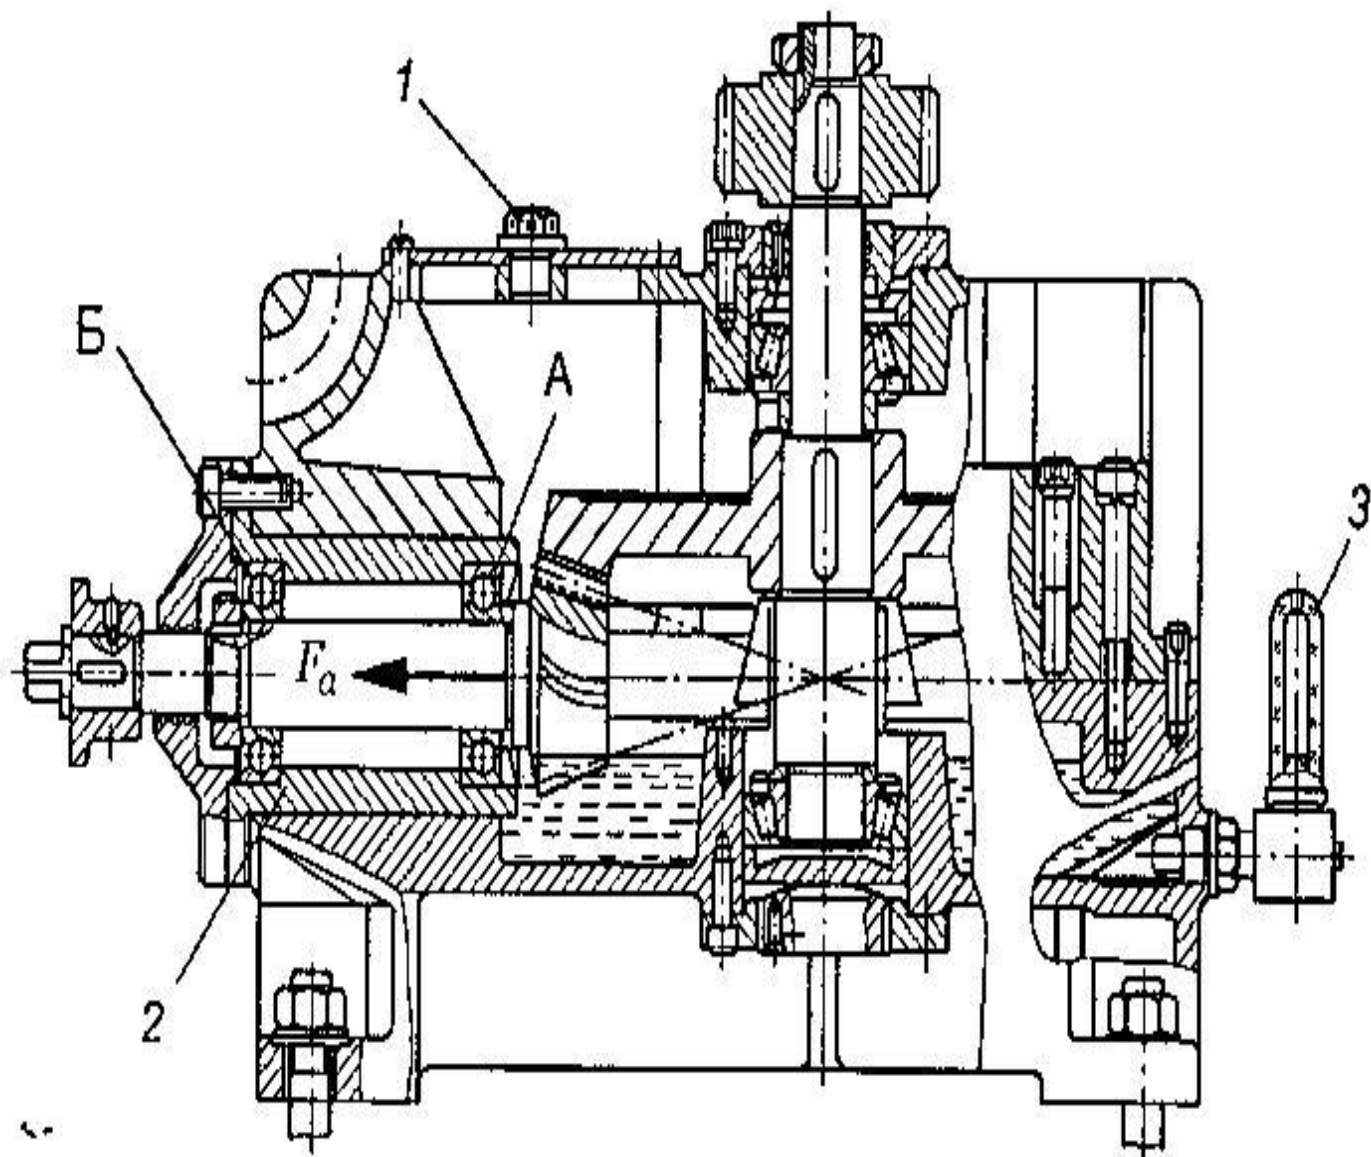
Конический редуктор с вертикальным расположением тихоходного вала:
